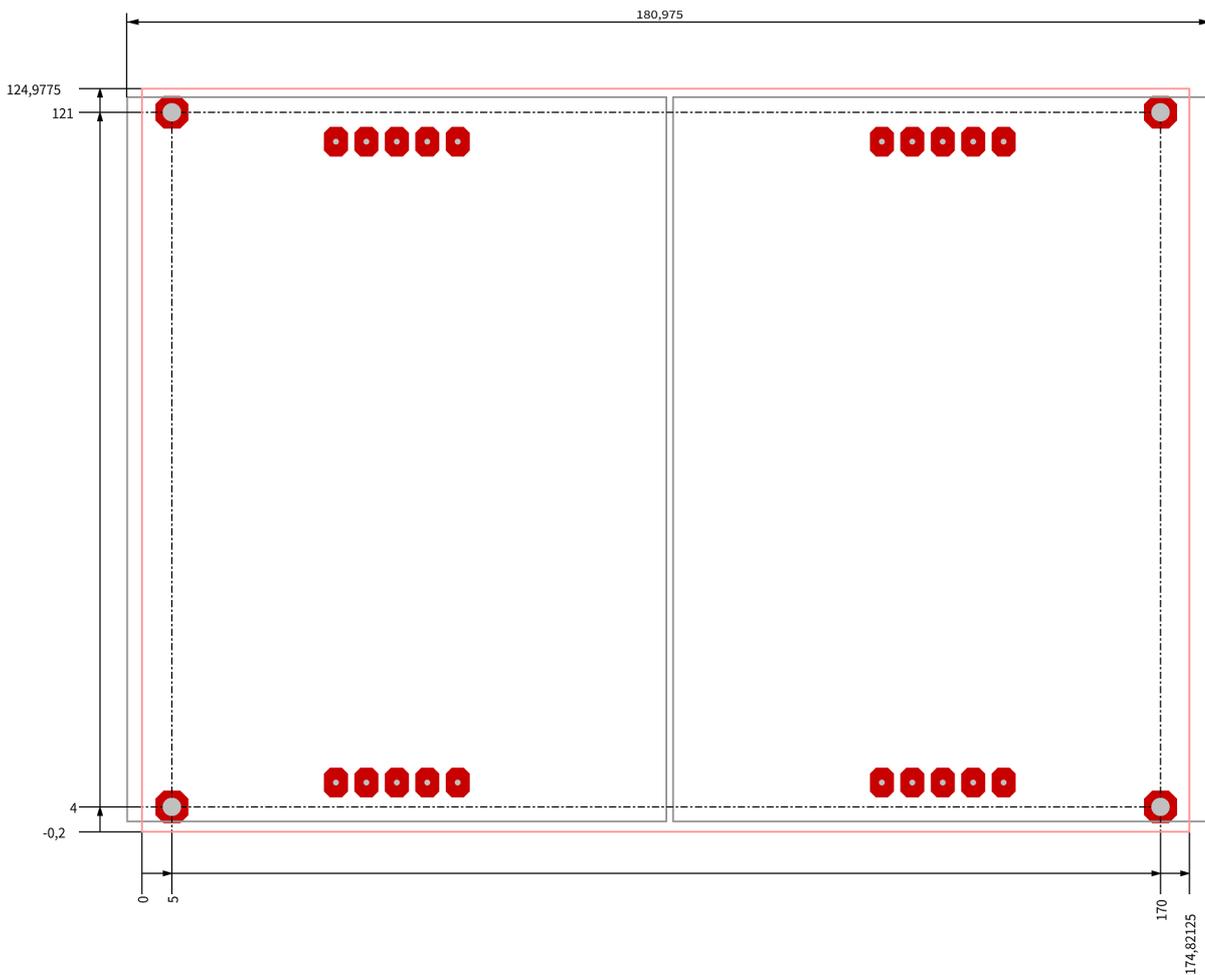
Beschreibung zum Einbau (Abmessungen) des Moduls PCB3100
